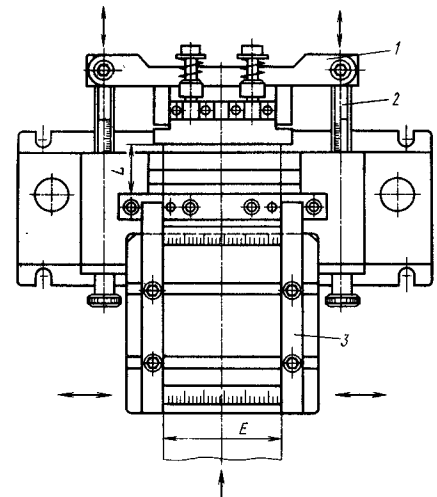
План конструкции универсально-переналаживаемого штампа для отрезки заготовок (B — ширина ленты; L — шаг подачи)
